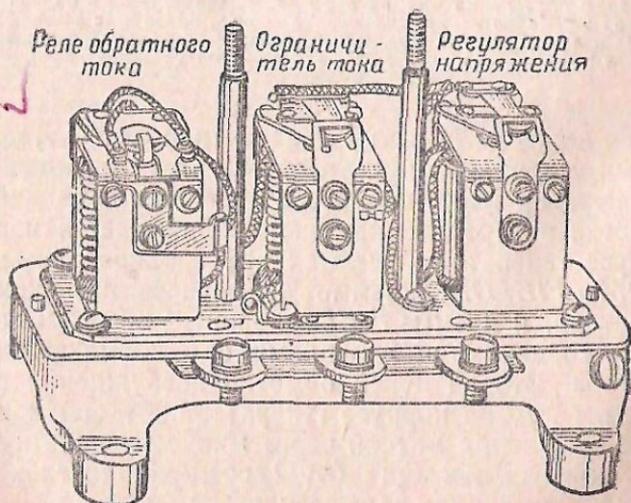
Общий вид реле-регулятора (со снятой крышкой)
